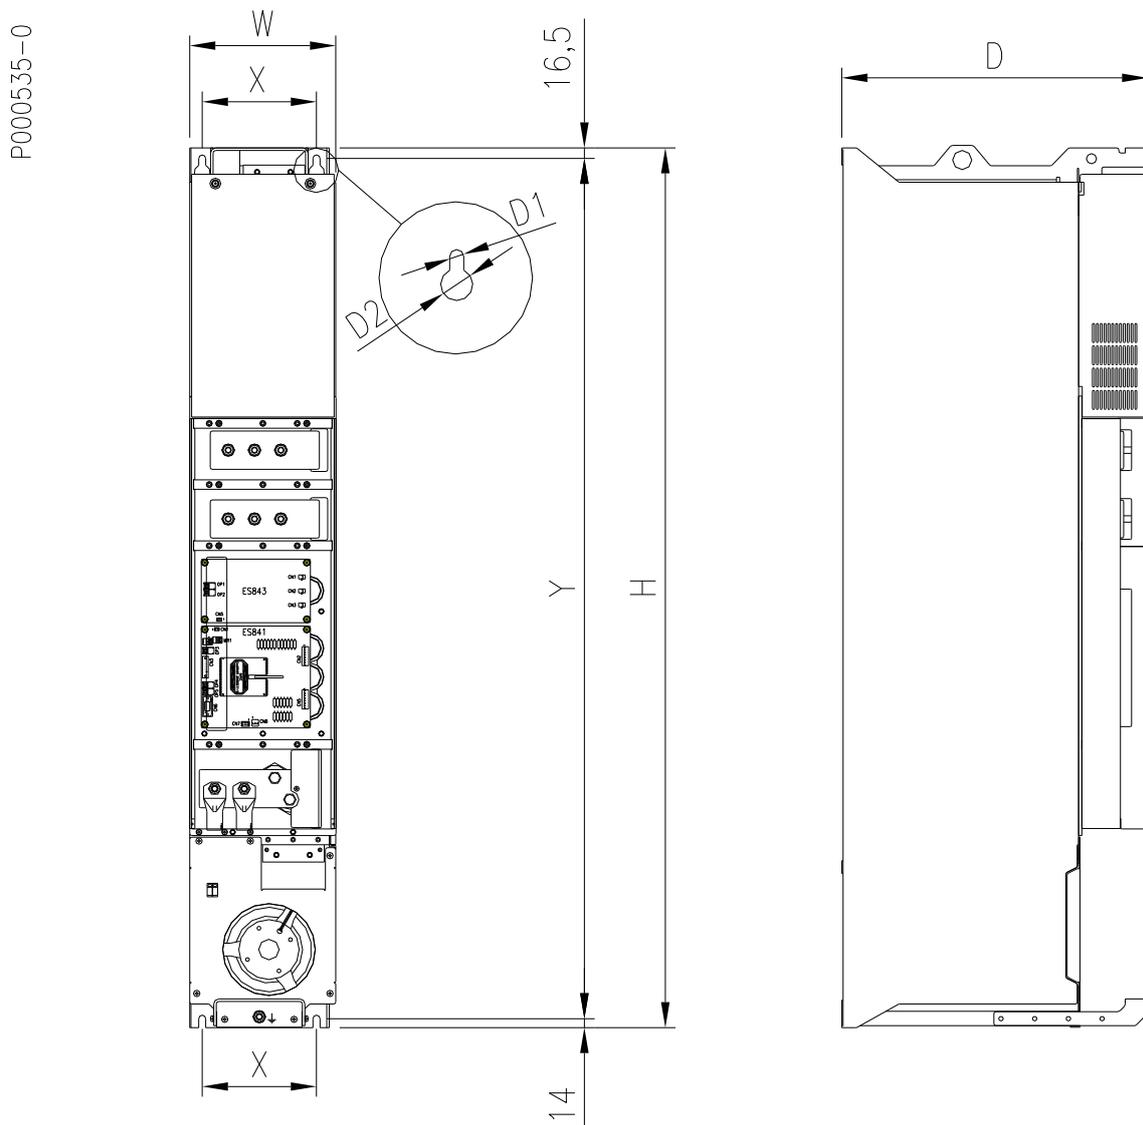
Dimensioni e punti di fissaggio del modulo BU1440
